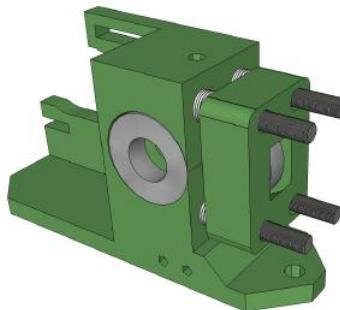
Ensamblado del cuerpo del extrusor (paso 4)
